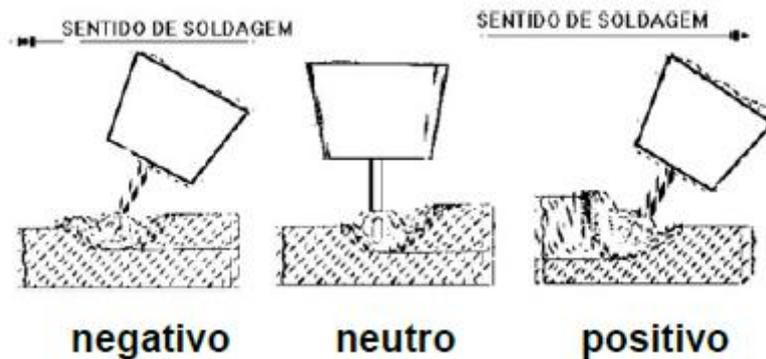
Sentidos de Soldadura Possíveis na Soldadura MIG [36]
